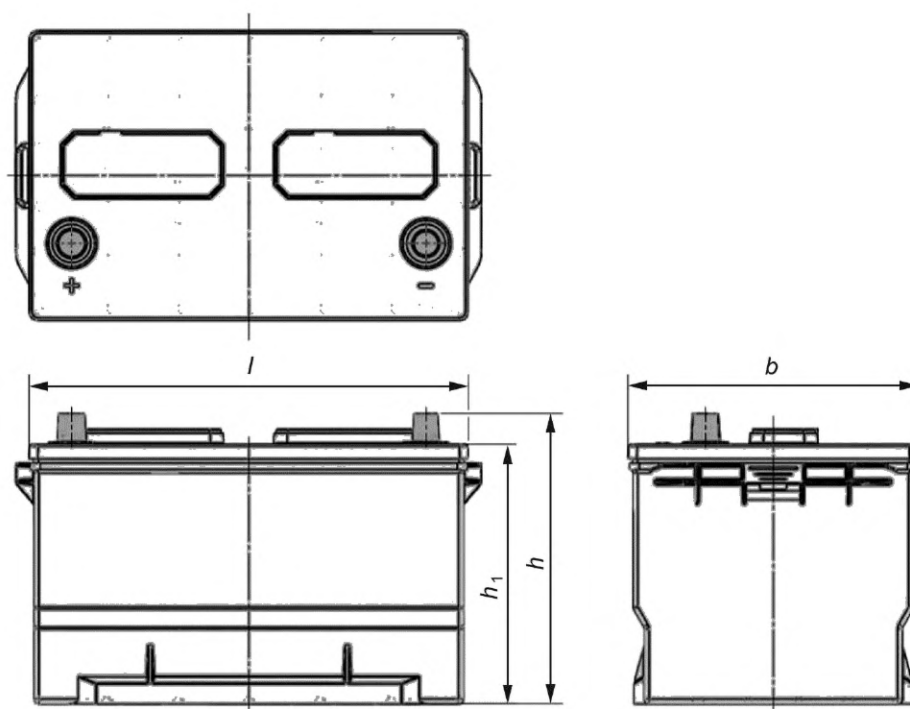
Основные размеры батарей типоразмеров 59, 65
